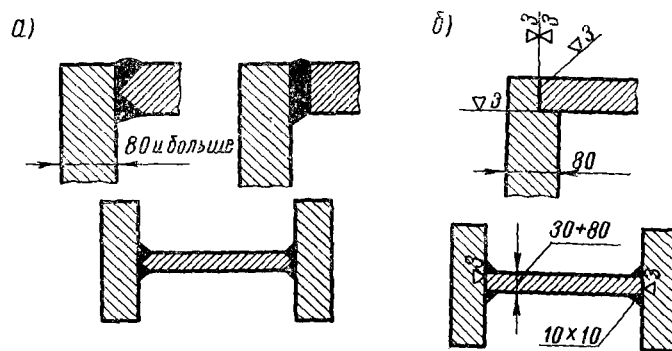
Сварные соединения станин прессов, выполненных из толстолистового проката:
